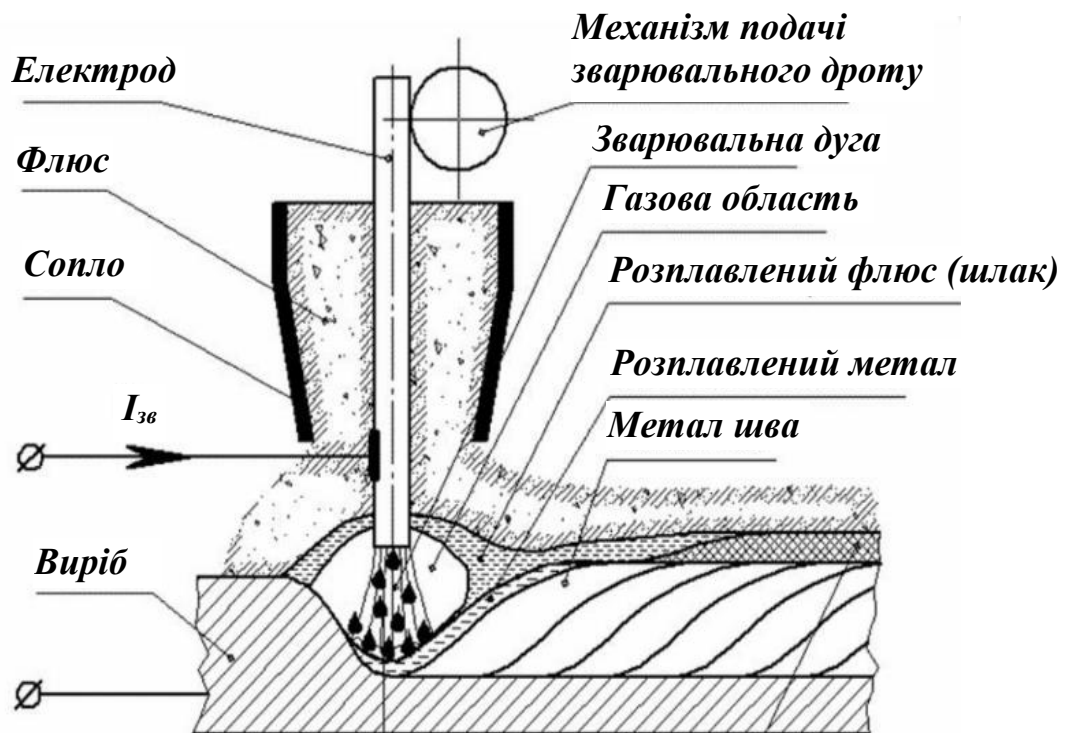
Принципова схема електрошлакового зварювання
